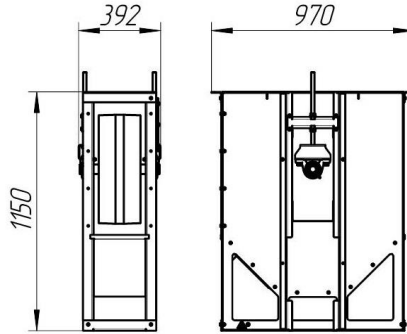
Станция натяжная нории Н-25. Размеры габаритные
